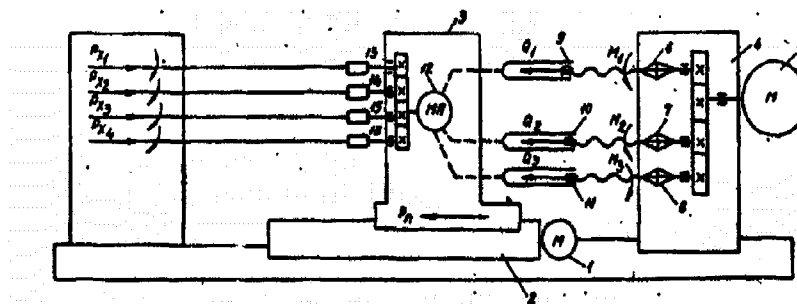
Силова багатошпindelна головка з механізмом для усунення пружних деформацій
